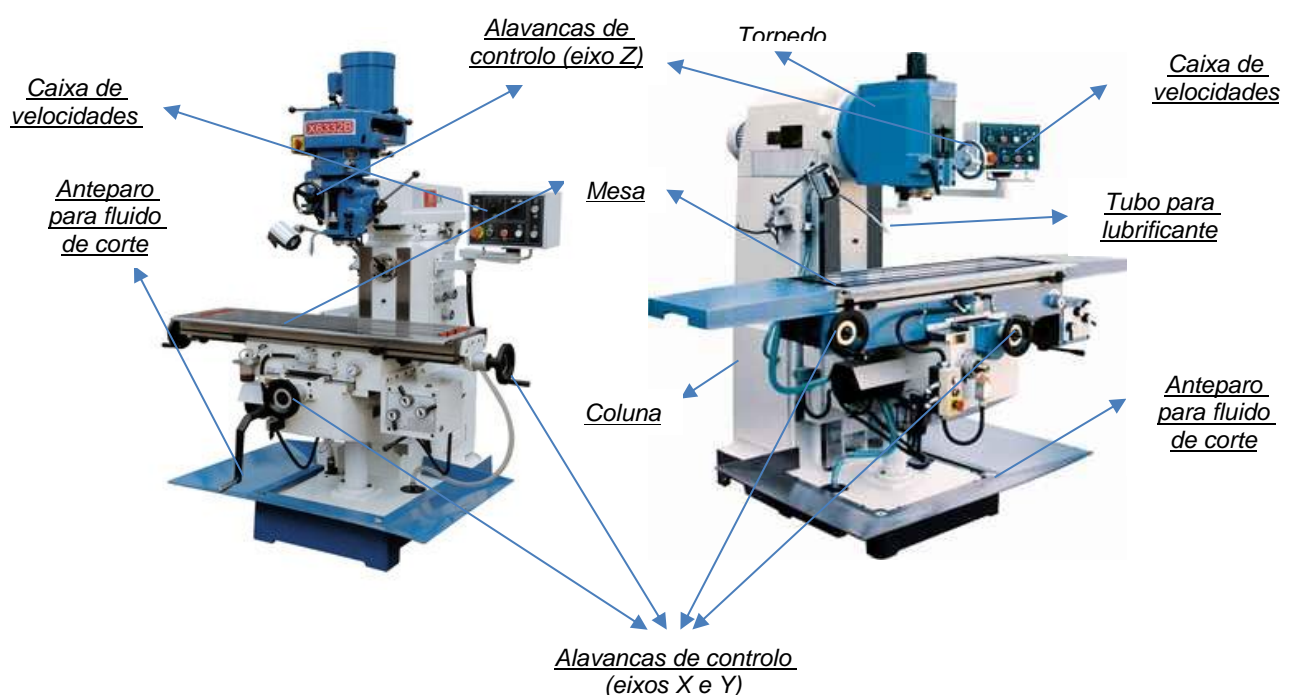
Máquina fresadora vertical (à esquerda), máquina fresadora horizontal (à direita) e seus constituintes (adaptada) [34-35]
